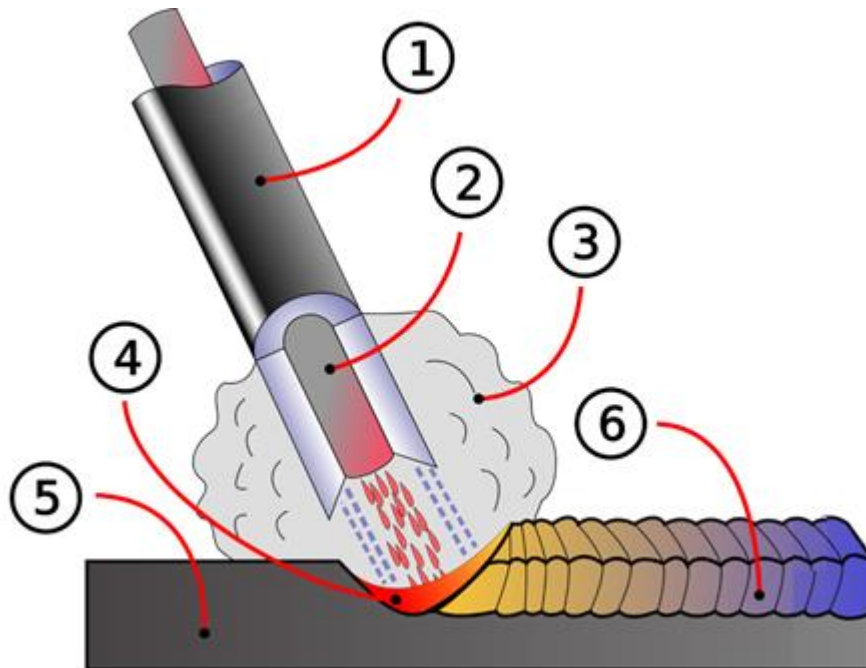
Soldagem a arco elétrico com eletrodo revestido: 1-Revestimento de Fluxo / 2-Vareta (Alma) / 3-Gás de proteção / 4-Poça de fusão / 5-Metal base / 6-Metal de solda [8]
